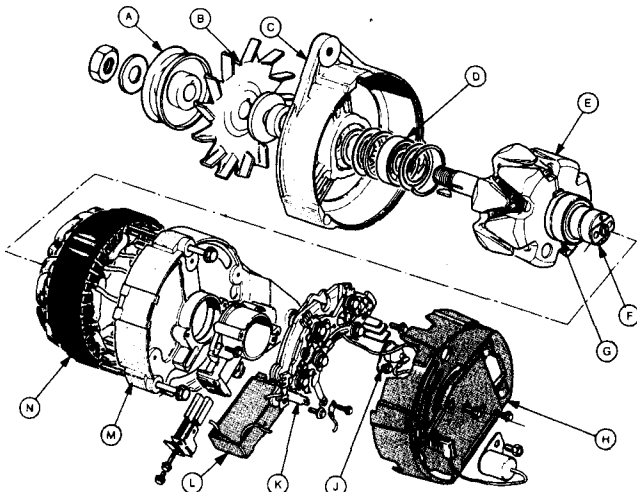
Генератор LUCAS A 133. А - Шкив. В - Вентилятор. С - Корпус. D - Подшипник. Е - Ротор. F - Стопорные кольца. G - Стопорное кольцо подшипника. Н - Крышка. J - Диод защиты от повышения напряжения. К - Выпрямитель. L - Регулятор. M - Стопорное кольцо. N - Статор.
